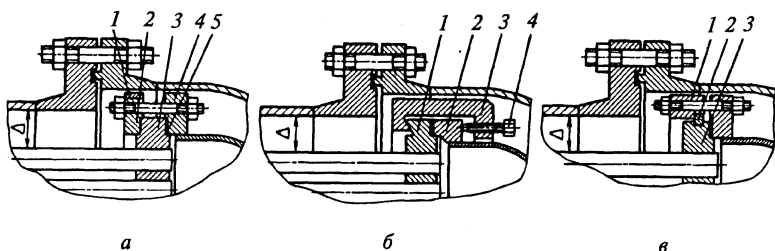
Способы крепления крышки плавающей головки к трубной решетке: а — разрезным фланцем; б — разрезной фланцевой скобой; в — разрезным кольцом
